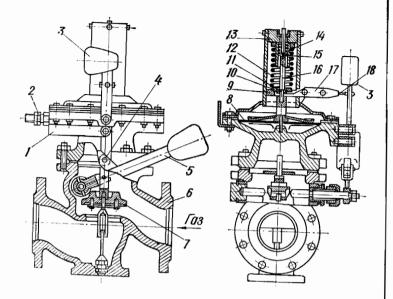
Предохранительно-запорный клапан типа ПКН (ПКВ): 1— анкервый рычаг; 2— штуцер; 3— молоточек; 4— штифт рычаг; 5— рычаг; 6— корпус; 7— клапан; 8— мембрана; 9— крышка; 10— тарелка; 11— шток; 12— пружина верхнего предела; 13— регулировочный винт; 14— пружина нижиего предела, 15— гайка; 16— шток; 17— коромысло; 18— штифт молоточка.
